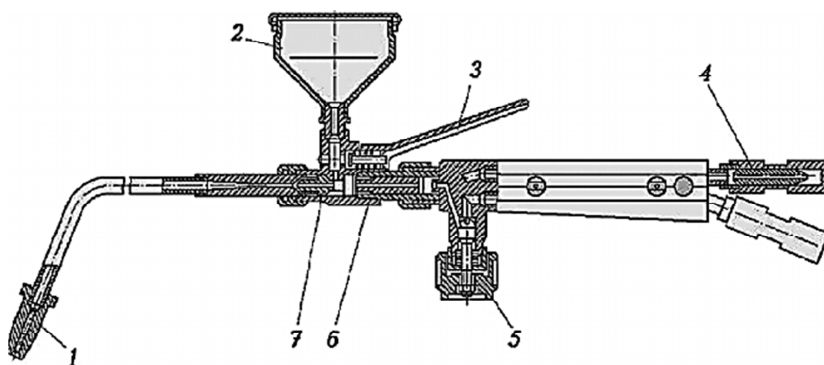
Устройство горелки марки ГН-2 для газопорошковой наплавки:
